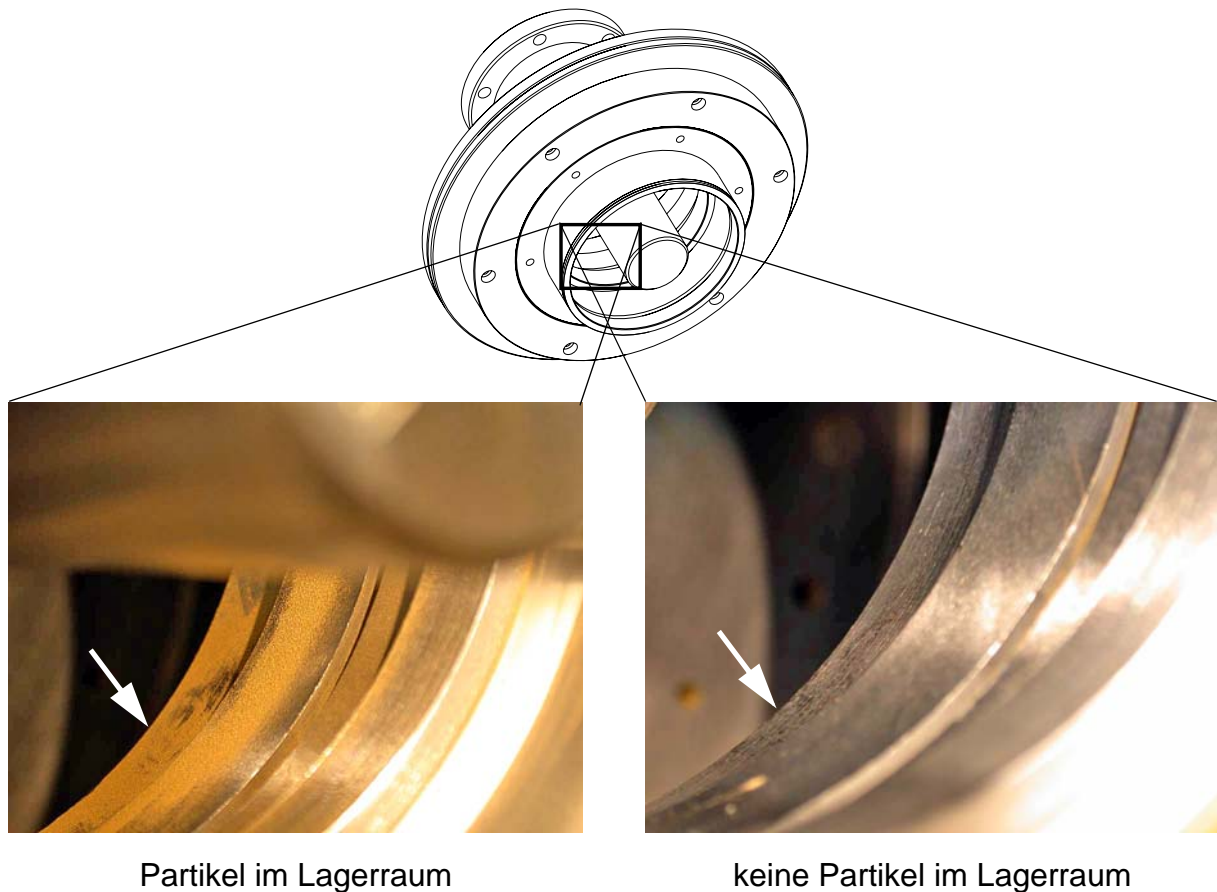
Lagerraum nach dem Schließen der Kammer, links mit Druckstoß, rechts ohne Druckstoß
